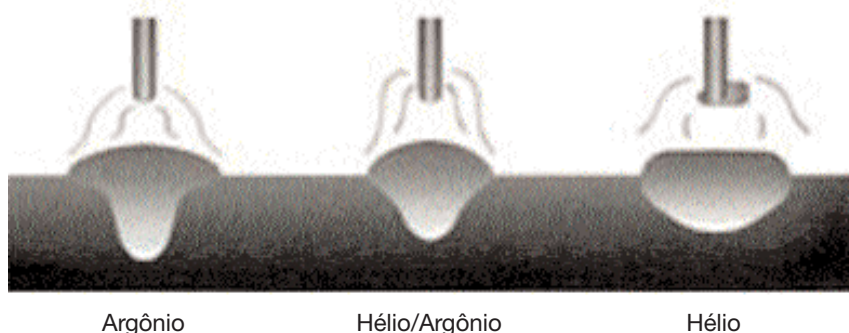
Perfis de solda GMAW com diferentes atmosferas de proteção.
